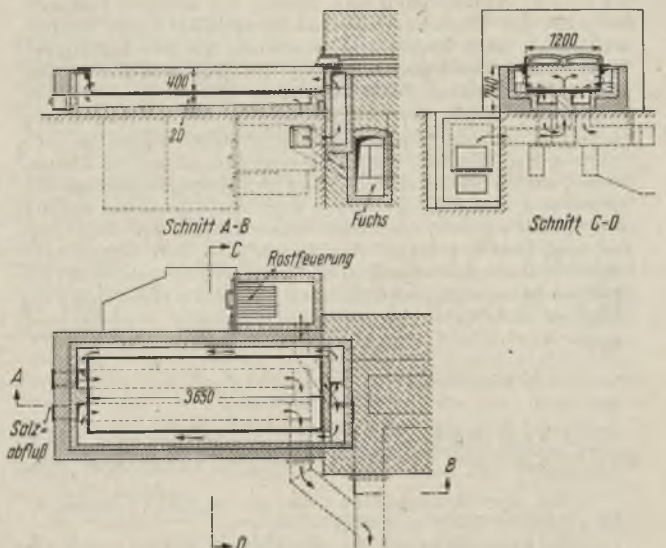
Salzbadwanne mit unmittelbarer Kohle- oder Koksfeuerung.
